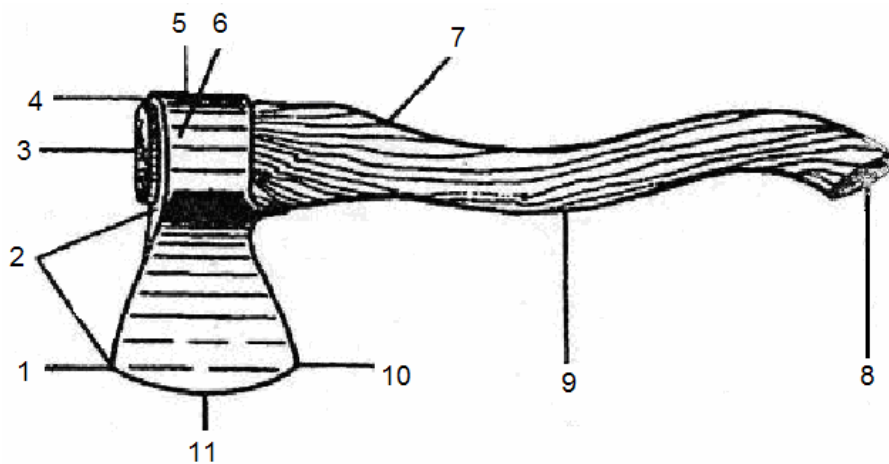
Топор: 1 – носок; 2 – клин; 3 – клин топорика; 4 – головка; 5 – обух топора; 6 – боковая стенка ушка головки; 7 – щека клинка; 8 – конец топорика; 9 – топориче; 10 – пятка; 11 – лезвие
